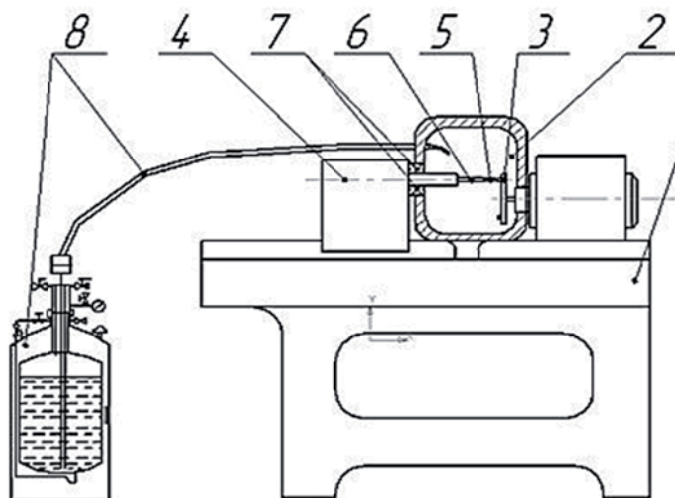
Установка для получения порошка высокоскоростным способом (1 – рама; 2 – камера для сборки; 3 – шлифовальный круг; 4 – устройство подачи; 5 – заготовка; 6 – оправка; 7 – защитные элементы; 8 – устройство подачи жидкого азота в зону обработки)
